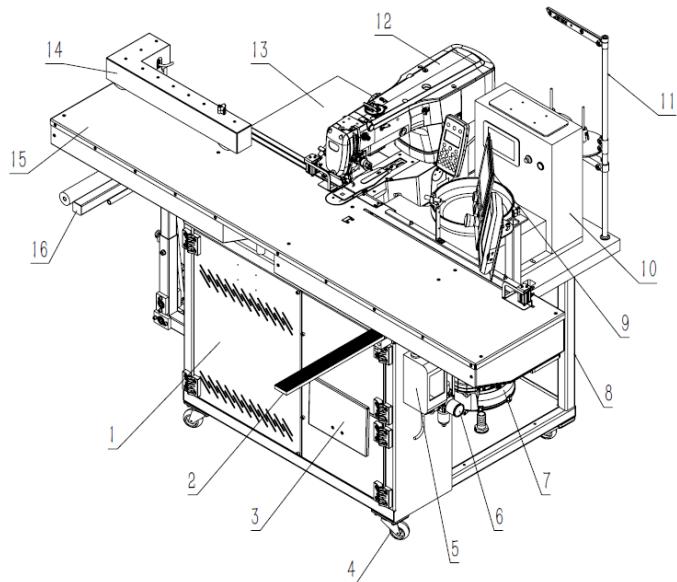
各部件展示图 Figure 2.1 Parts Display Drawing
